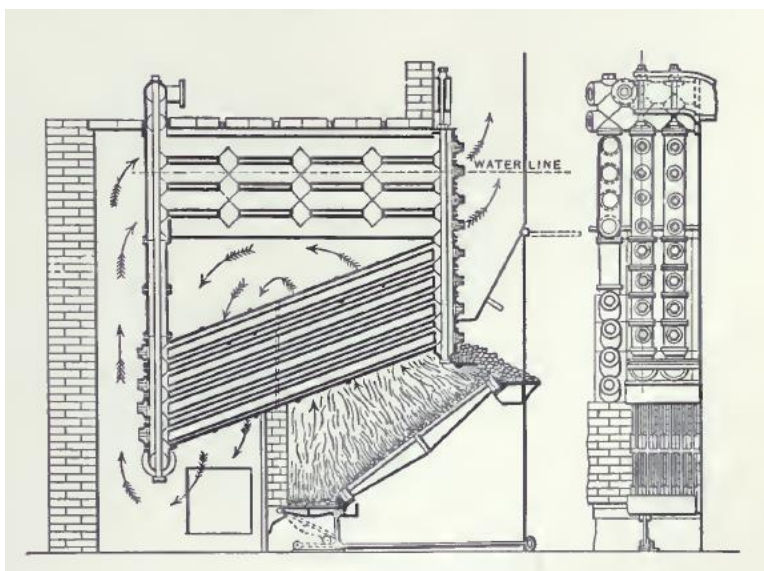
Desenho técnico da primeira caldeira Babcock & Wilcox, de 1867 (*The Babcock & Wilcox Company*, 1922, p. 39)
